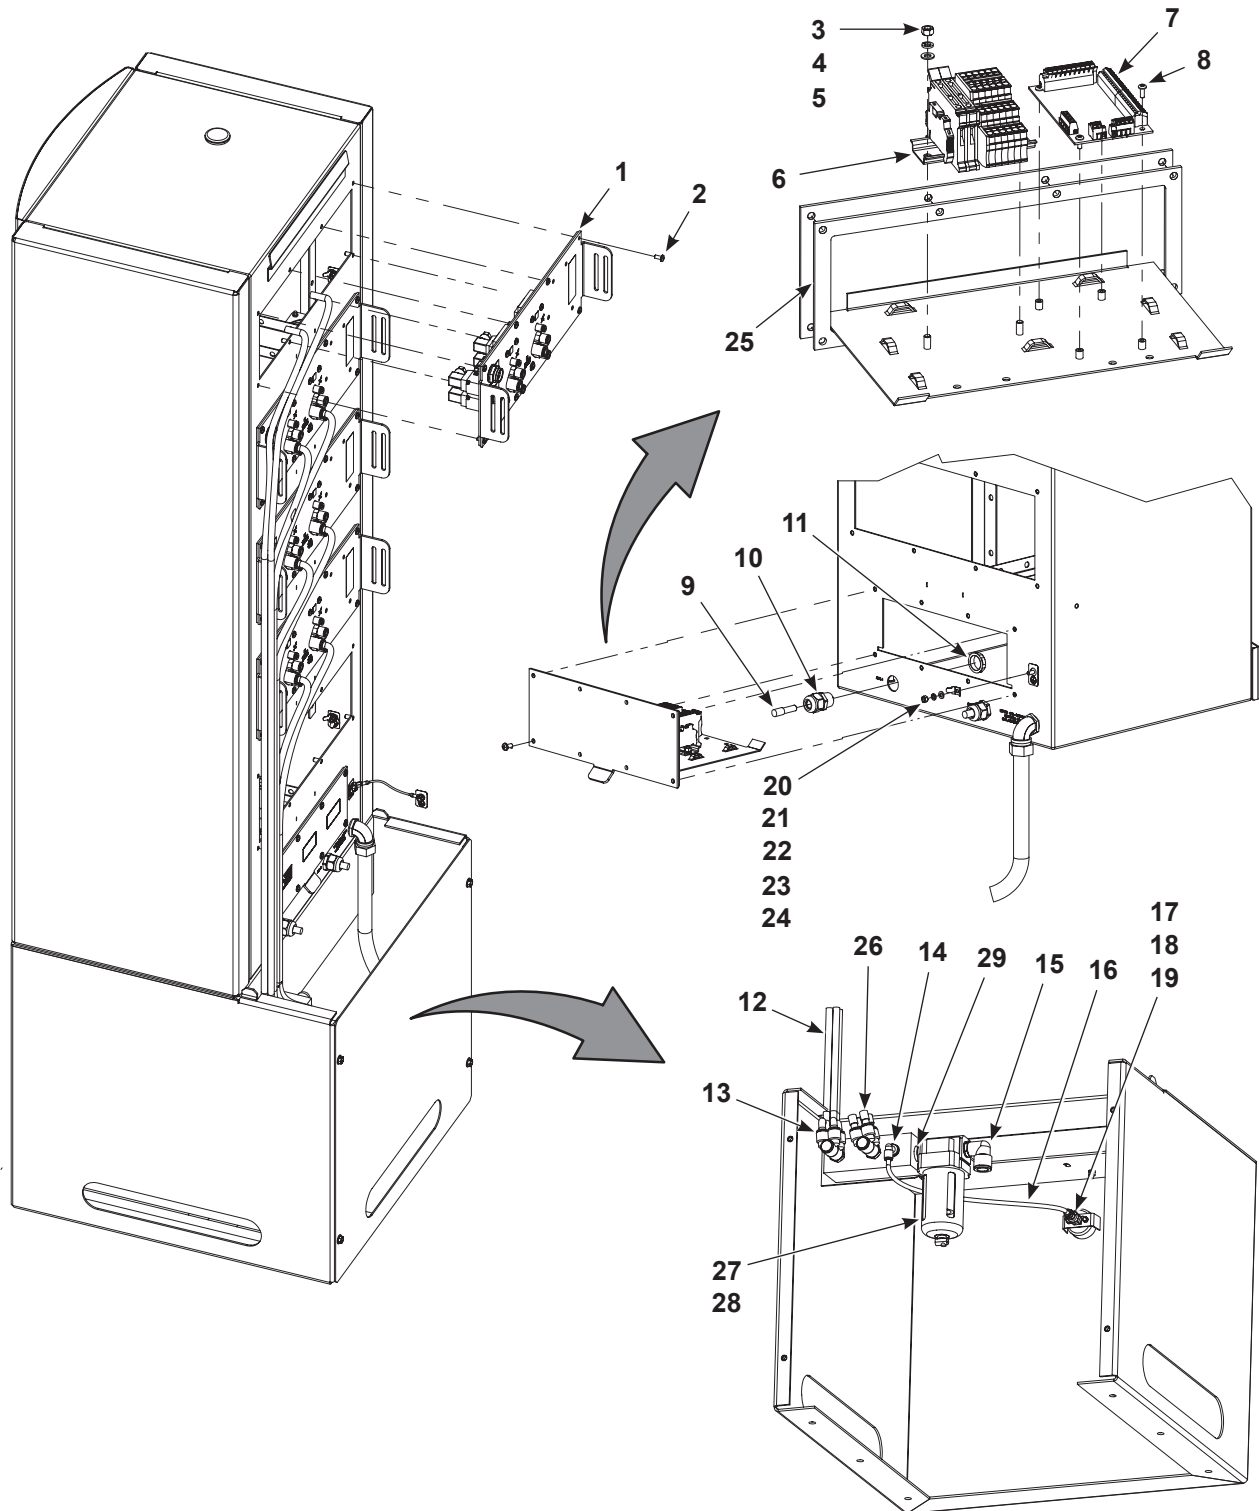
Pièces du panneau arrière du contrôleur pour plusieurs pistolets
